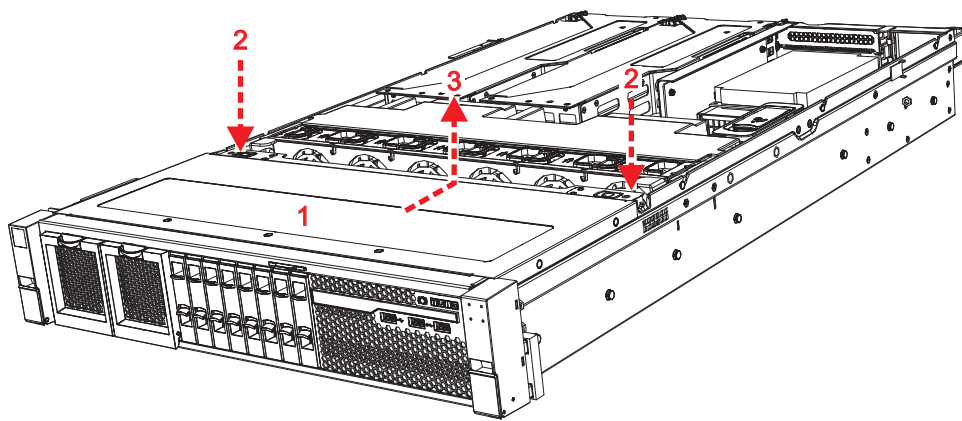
Removendo a tampa frontal superior do 2145-SV1
